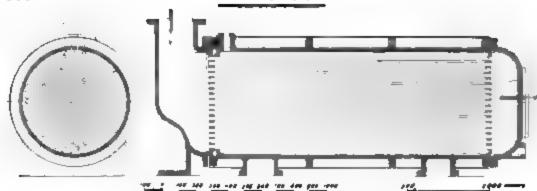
1568. Receiver für Tandemmaschine. d = 625; D = 1080 H = 1250; n = 56.*)
